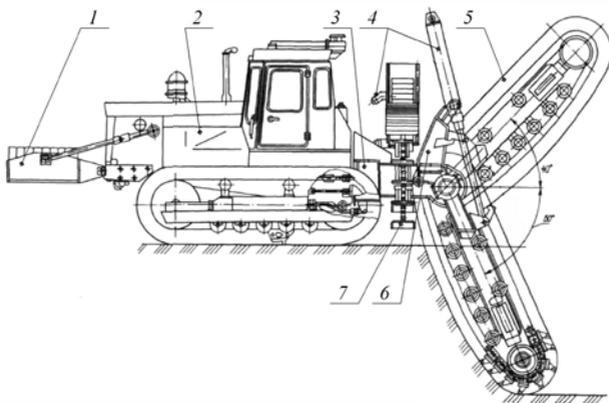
Экскаватор-траншеекопатель ЭТЦ-208: 1 – противовес; 2 – трактор базовый; 3 – редуктор привода; 4 – гидросистема; 5 – рабочее оборудование; 6 – рама; 7 – поперечный скребковый конвейер
